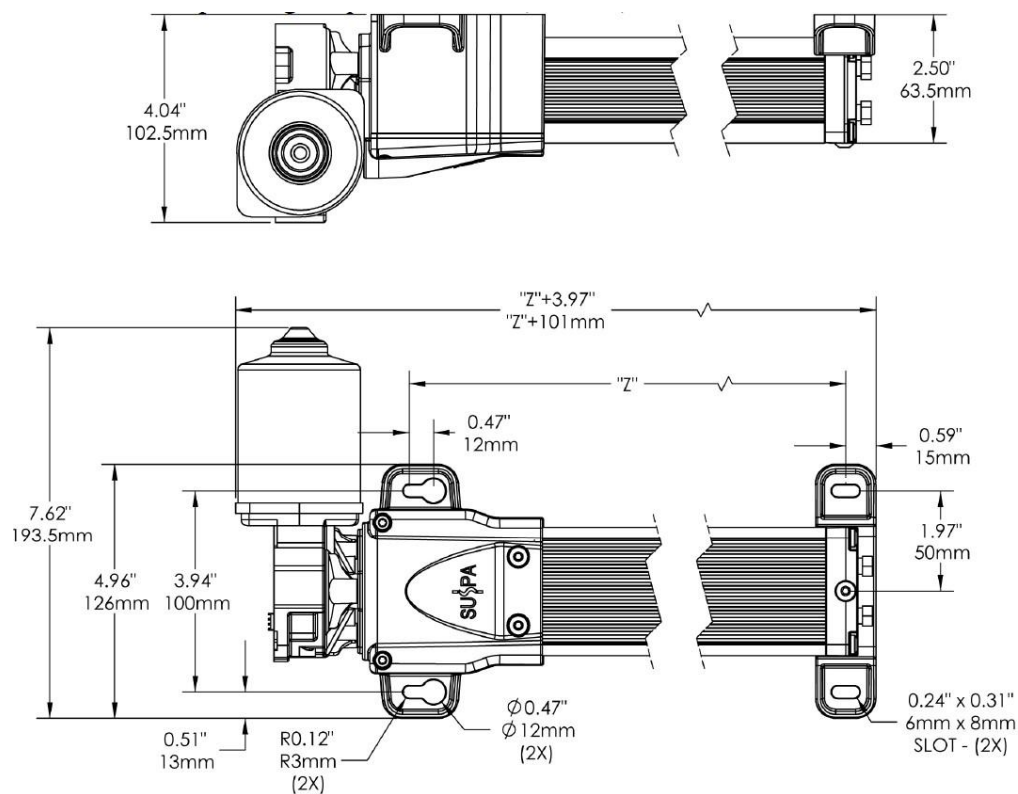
Abmessungen / Anschlüsse der Motorpumpe
